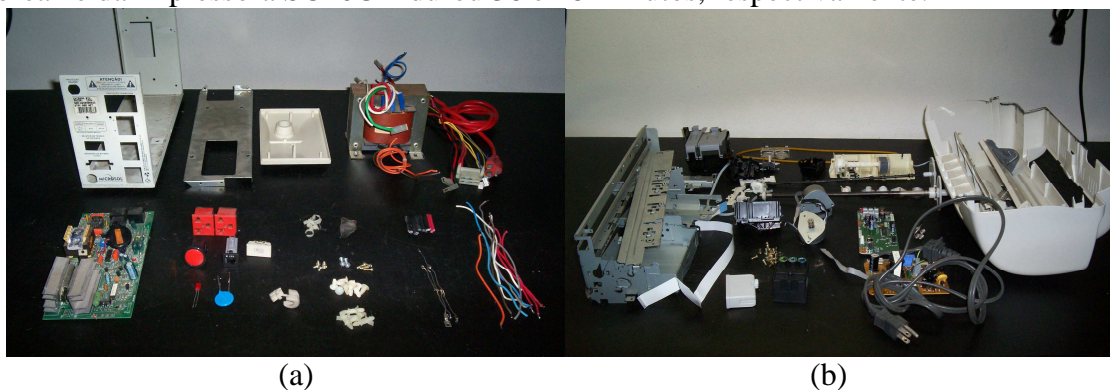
(a) *No-break stay 600* desmontado. (b). Impressora *SC C20UX* desmontada.
